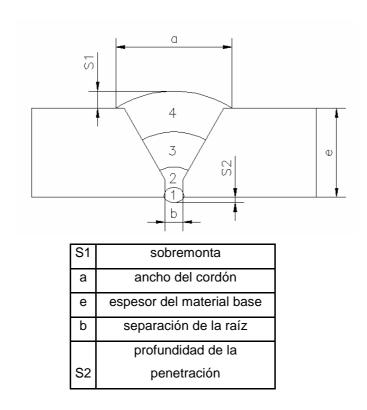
Bisel y posición de los cordones de soldadura
